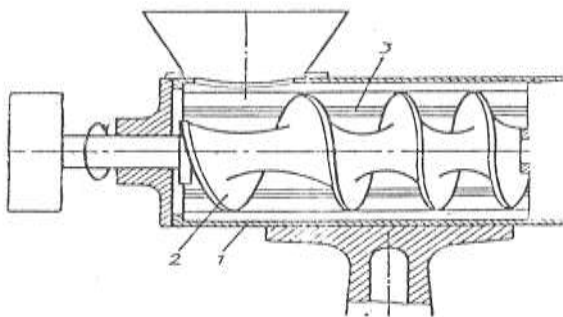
Подающий механизм: 1- рабочая камера; 2- шнек; 3- ребра
